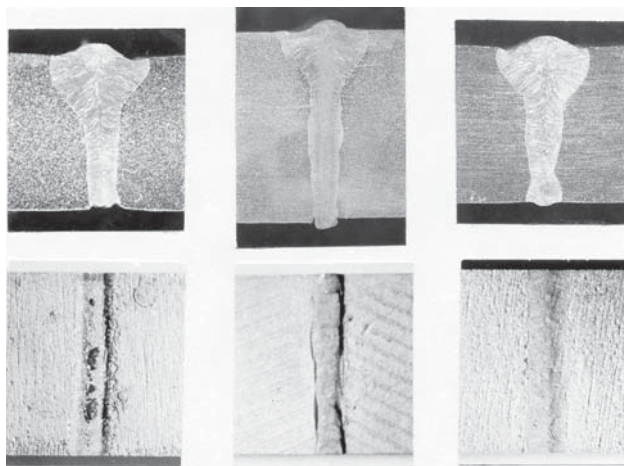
Макрошлифы и внешний вид поверхности обратного валика сварных швов, выполненных CO₂-лазером без его защиты (а), с защитой гелием (б) и аргоном (в). Сталь марки 08Х18 Н10 Т толщиной 10 (а, в) и 12 мм (б). Скорость сварки 0,72 м/мин, фокусировка на поверхности детали, мощность 9 (а, в) и 10,5 (б) кВт. Защитный газ со стороны лицевого валика — гелий [9–11]
